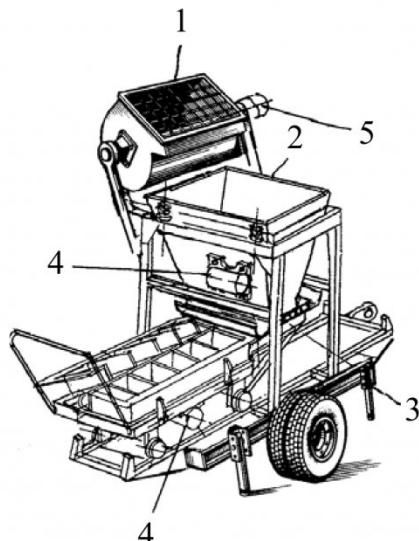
Прицепной смесительно-формовочный агрегат: 1 – смеситель; 2 – челночный станок с ручной подачей; 3 – шасси; 4 – электро- или гидровибраторы; 5 – электро- или гидромотор
